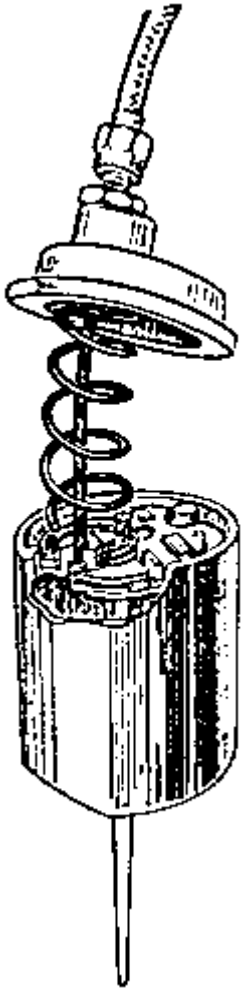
Der Nadelhalter mit Teillastnadel muß auf dem Gasschieberboden plan aufliegen, er wird durch die Druckfeder gehalten.
